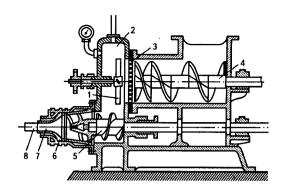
Ленточный вакуум-пресс: 1 – смесительная камера; 2 – вакуум-камера; 3 – перфорированная перегородка; 4 – лопастной винт; 5 – шнековый вал; 6 – прессующая головка; 7 – мундштук; 8 – глиняный брус
